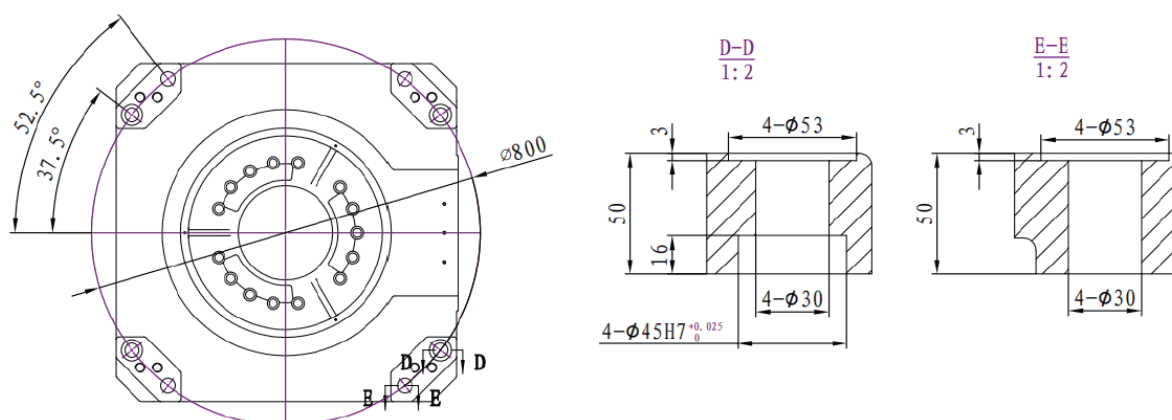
Габаритные чертежи робота-манипулятора SP120-2400.
